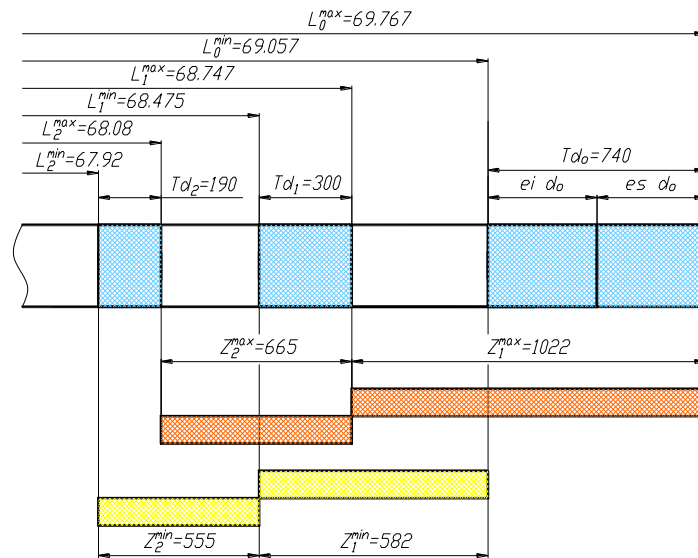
Схема розташування припусків та допусків на обробку площини 68
